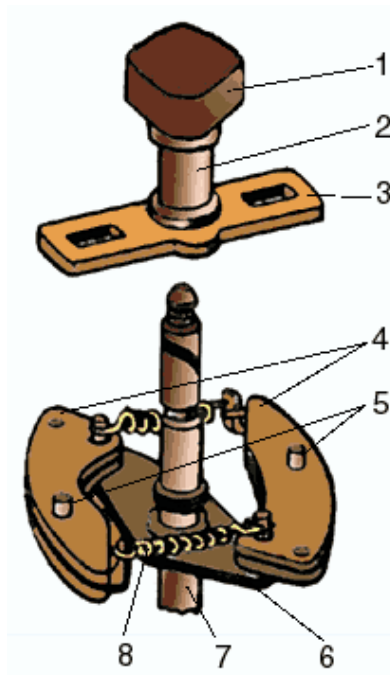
Конструкция центробежного регулятора угла опережения зажигания: 1 - кулачок прерывателя; 2 - втулка кулачков; 3 - подвижная пластина; 4 - грузики; 5 - шипы грузиков; 6 - опорная пластина; 7 - приводной алик; 8 – стяжные пружины
